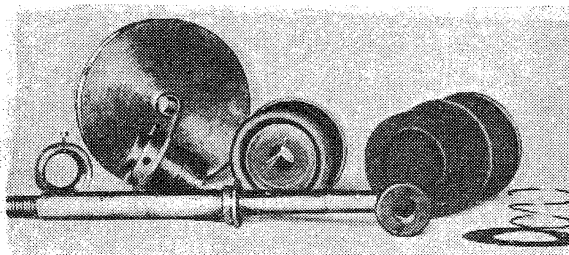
Б, В и Г. Внутренний диаметр детали Б по валу. Подшипник вала барабанов
